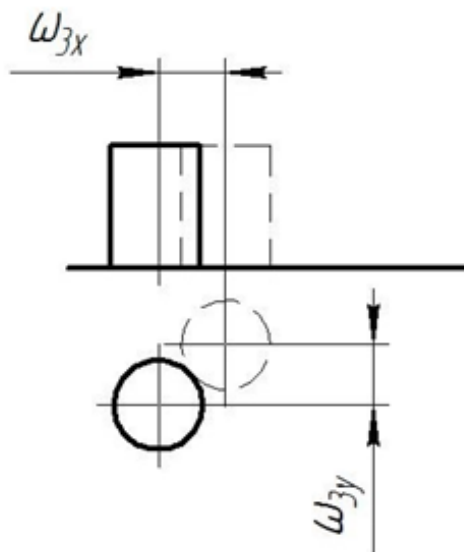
Похибка положення заготовки на проміжних позиціях
